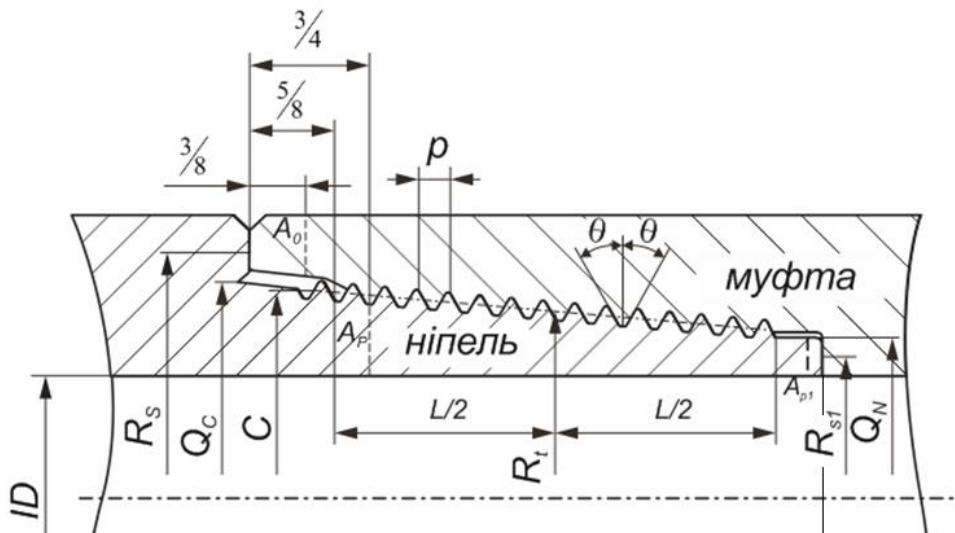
Розрахункова схема двоопорного ЗРЗ
